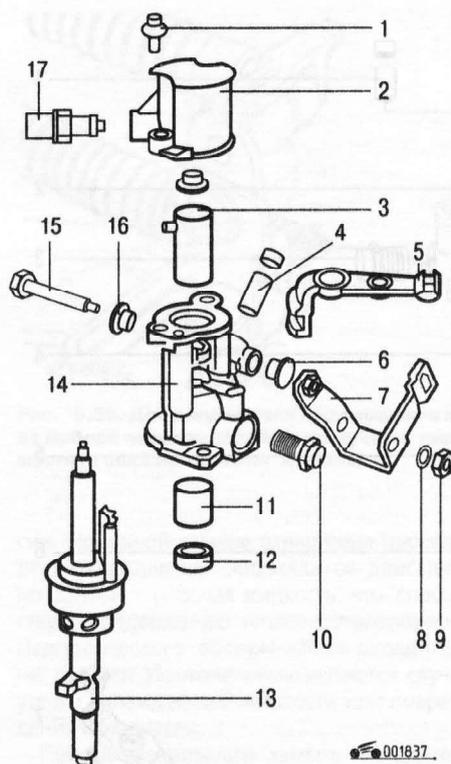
Механизм выбора передач: 1 – винт; 2 – крышка; 3, 4, 6, 16 – втулки; 5 – рычаг переключения передач; 7 – рычаг предварительного выбора передач; 8 – шайба; 9 – гайка; 10 – стопорный болт; 11 – опорная втулка; 12 – кольцо; 13 – вал механизма выбора передач; 14 – корпус; 15 – болт; 17 – выключатель фонарей заднего хода
